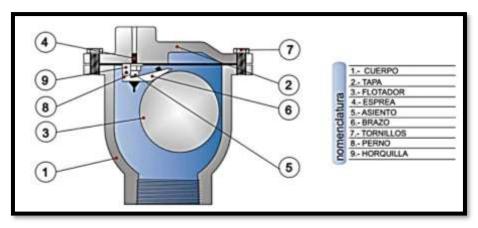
Partes de una válvula eliminadora de aire [Diisa 2018].
